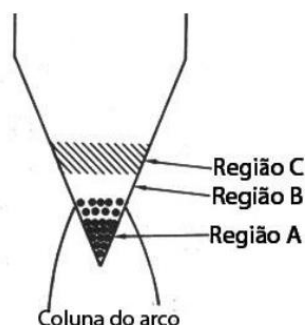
Regiões que compõem um eletrodo após a soldagem no processo TIG (SADEK ET AL.,1990)
